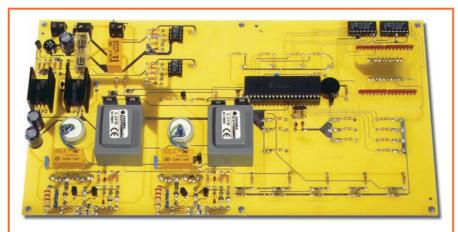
Photo d'un des prototypes de la platine de l'électrostimulateur vue du côté "composants".
